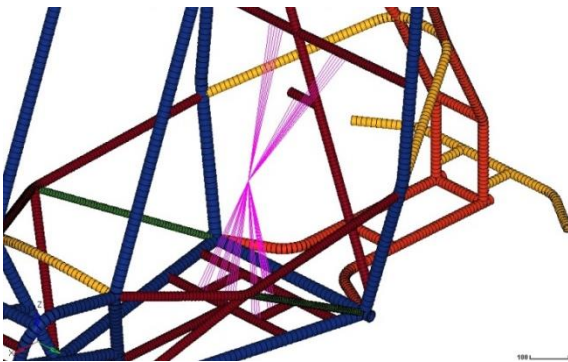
Elemento rígido en el centro de masa del vehículo. Vista detallada.
